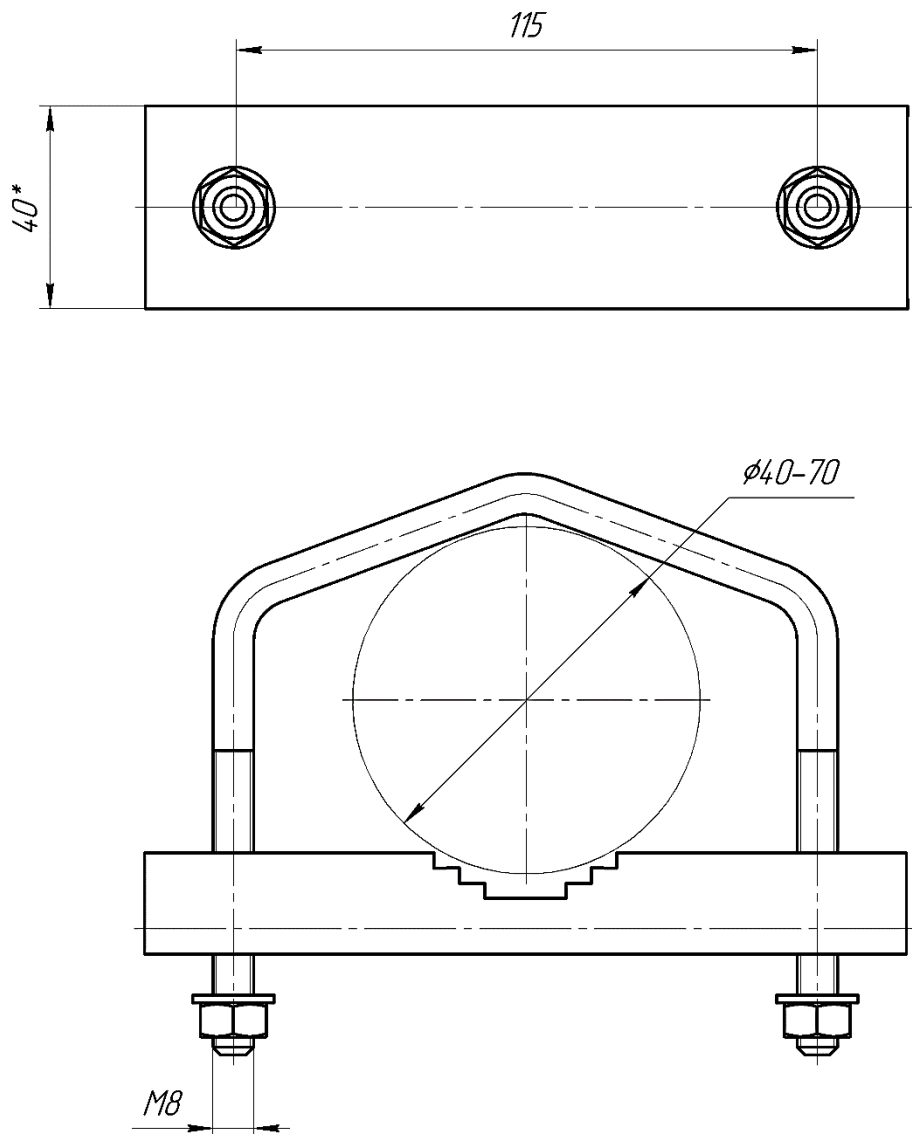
Чертеж пластины крепления ГА на трубу
